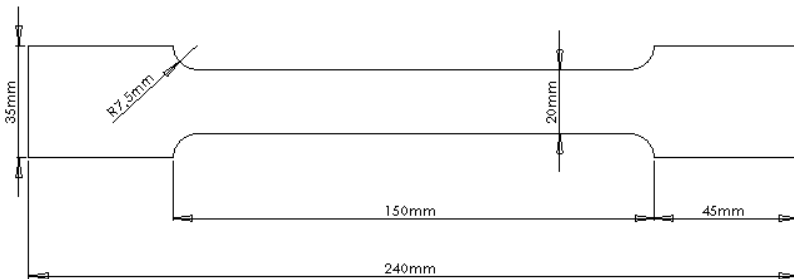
Dimensões do corpo de prova do ensaio de tração para a viga de PSAI.
